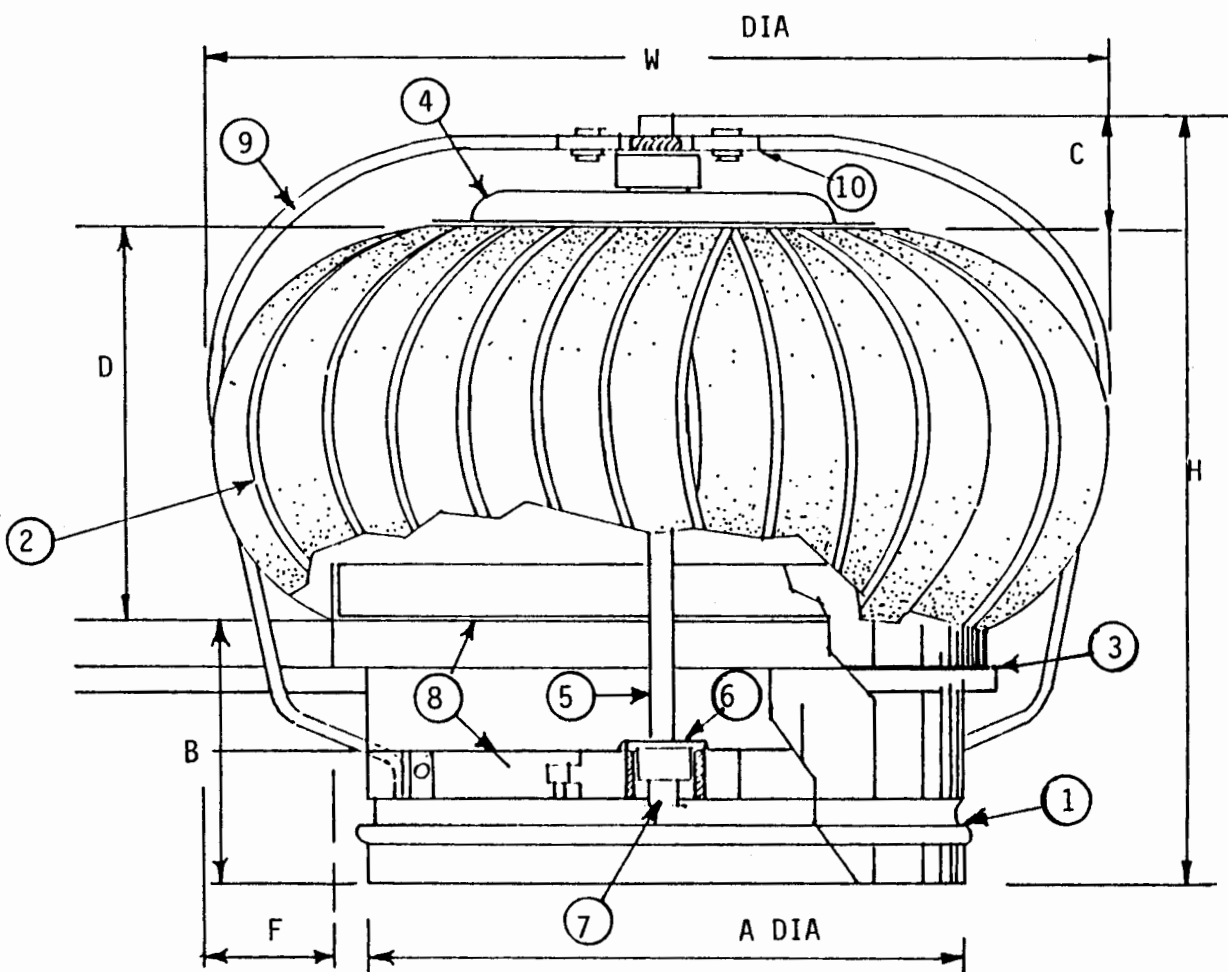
Principales dimensiones del Extractor Eólico.
